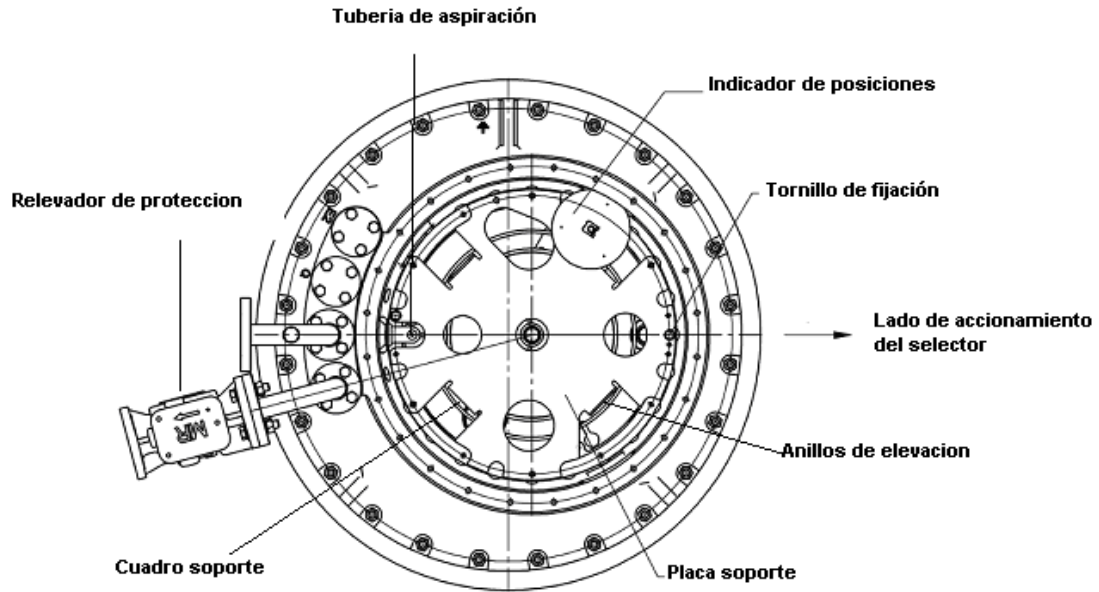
Disposición del relevador de protección e indicador de posiciones
